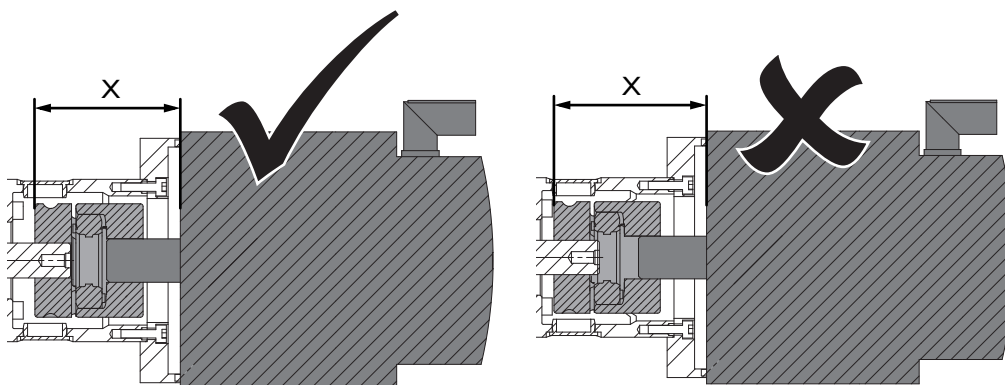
Установить муфту на вал мотора: Использовать допуск "Размер X"
